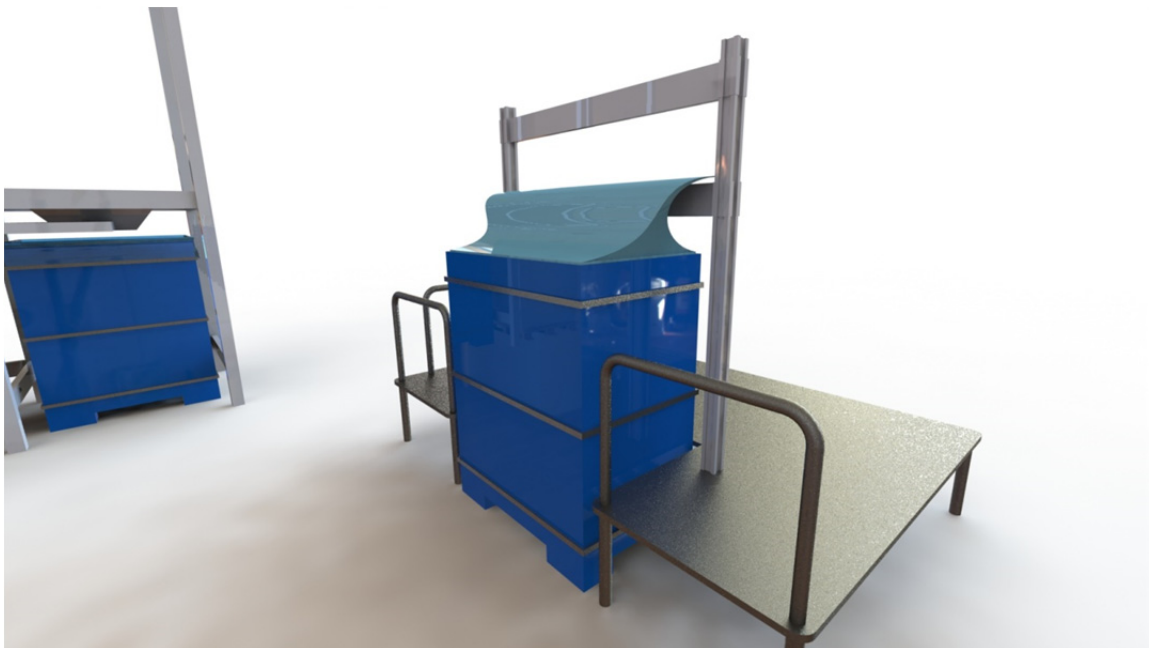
Molde con envase ProX colocado en la soldadora de barras.
